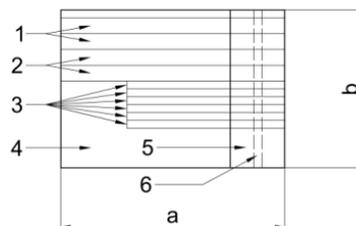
Probenlage bei Flächenschweißnähten als Überlappnaht
